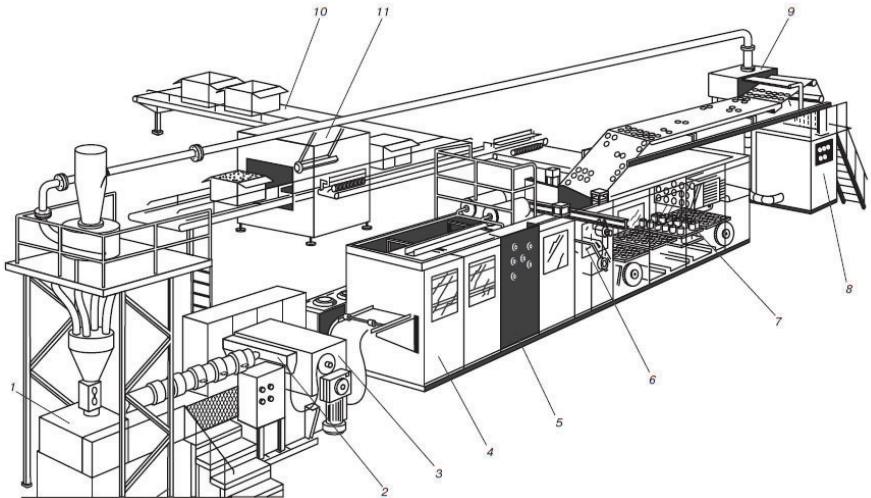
Загальний вигляд автоматичної лінії повного циклу формування
